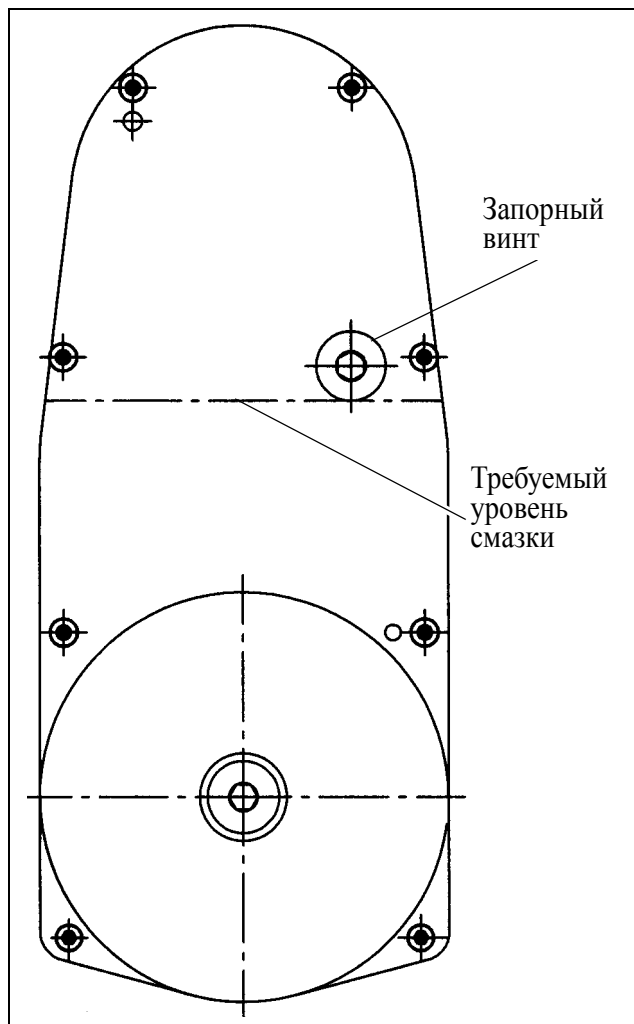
Поворотная консоль корпуса пилы в положении контроля количества смазки
